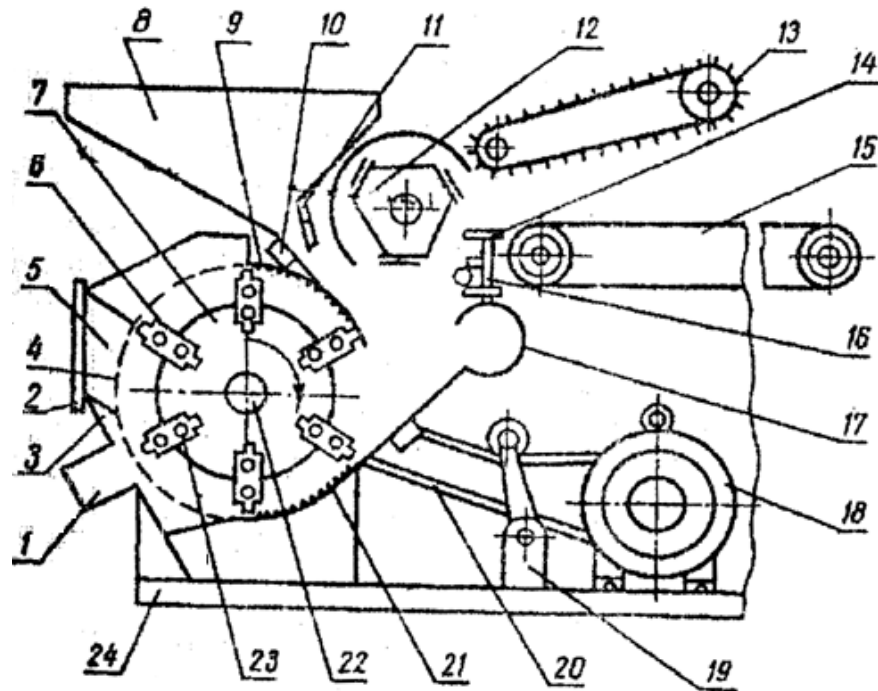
Схема дробарки КДУ-2: 1- відсосуючий патрубок; 2- кришка вивантажувального люка; 3- вставна викидна горловина; 4- решето; 5- кришка дробильної камери; 6-молоток; 7- диск ротора; 8- бункер; 9- верхня дека; 10- верхній магнітний сепаратор; 11-поворотна заслінка; 12- ріжучий барабан; 13- пресуючий транспортер; 17- підвідний повітряний патрубок; 18- електродвигун; 19- натяжний пристрій; 20- нижній магнітний сепаратор; 21- нижня дека; 22- вал ротора; 23- вісь; 24-рама» [9].
